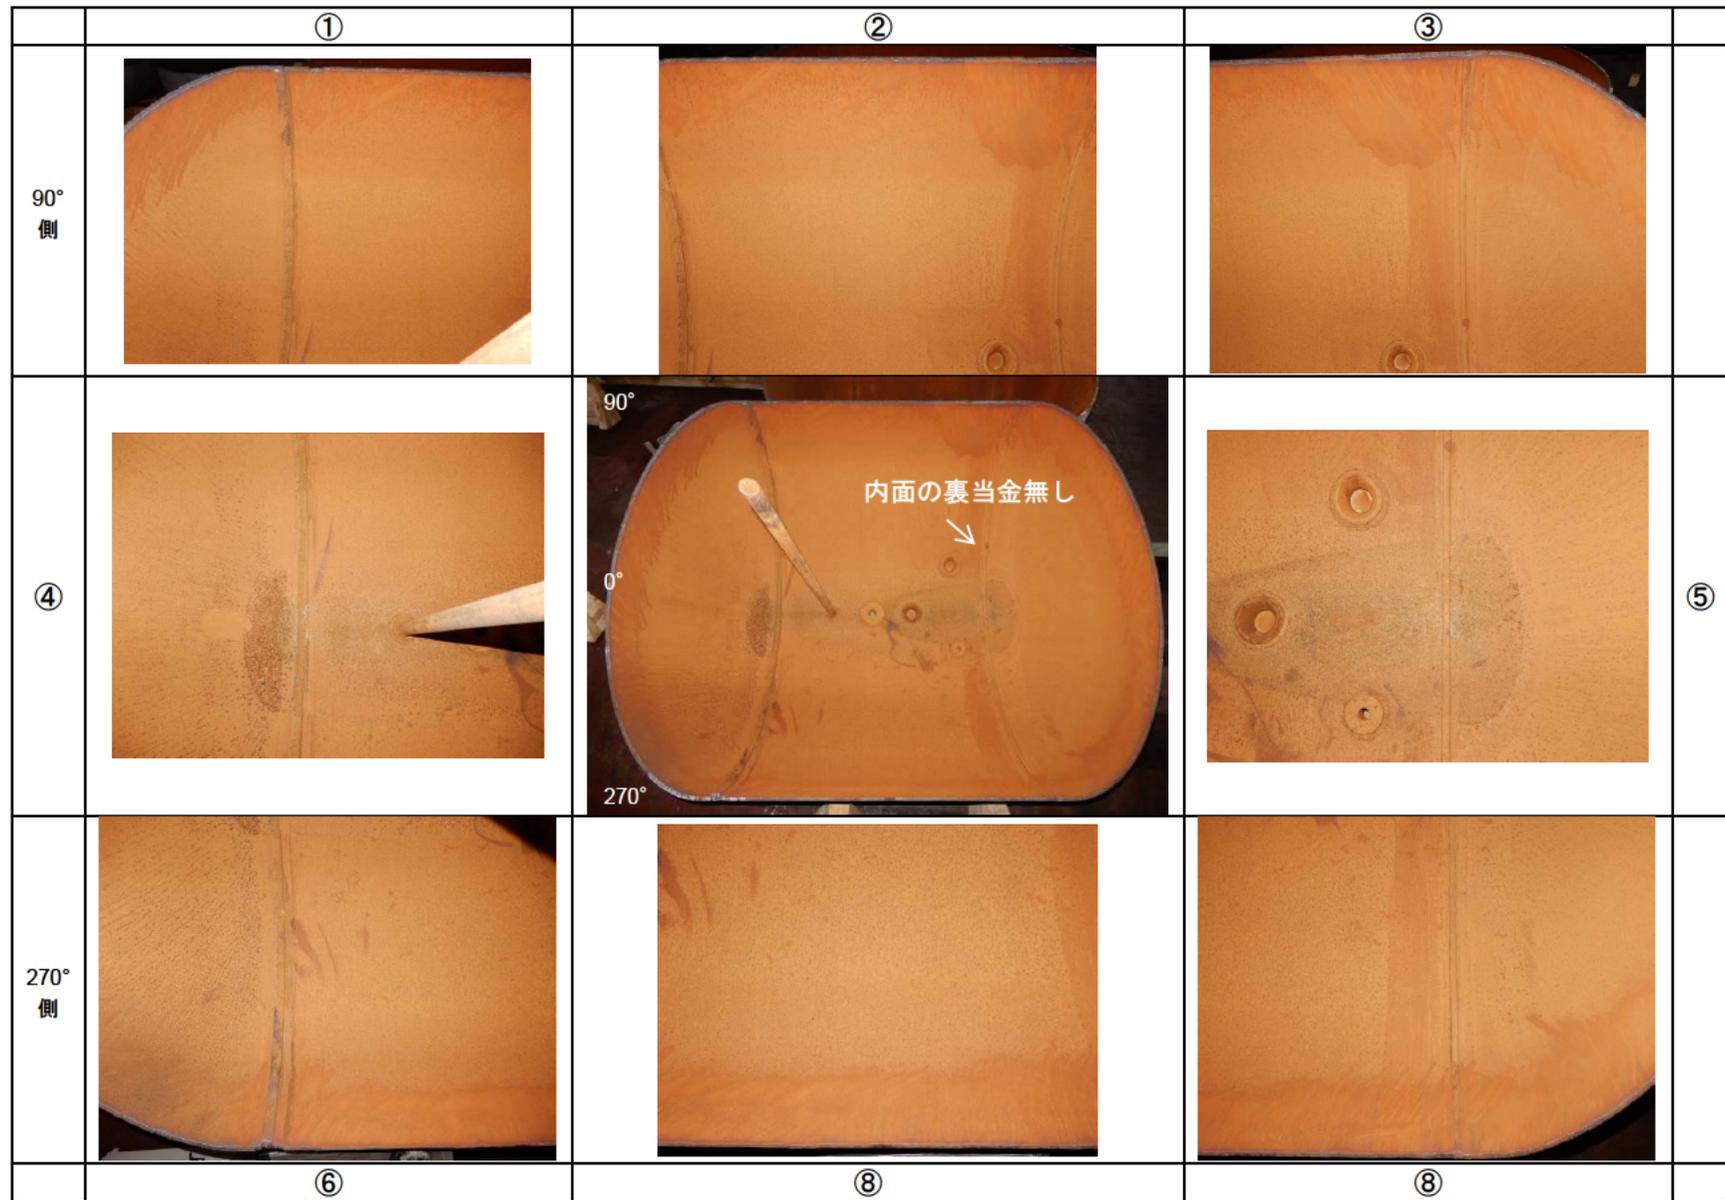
被試験体内面状況 C-1 (上部 (耐圧試験実施))
